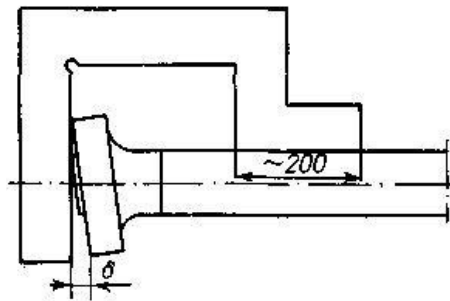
Проверка перпендикулярности уплотнительной поверхности фланца к оси трубы
